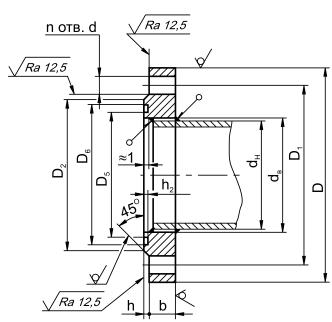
Размеры ответных фланцев для фильтров с присоединительными фланцами PN 16
